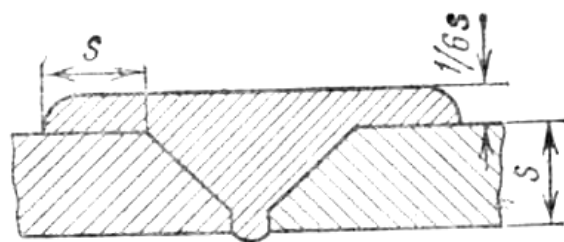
Зварювання чавунних деталей сталевими електродами зі збільшеною шириною підсилення зварного шва.
